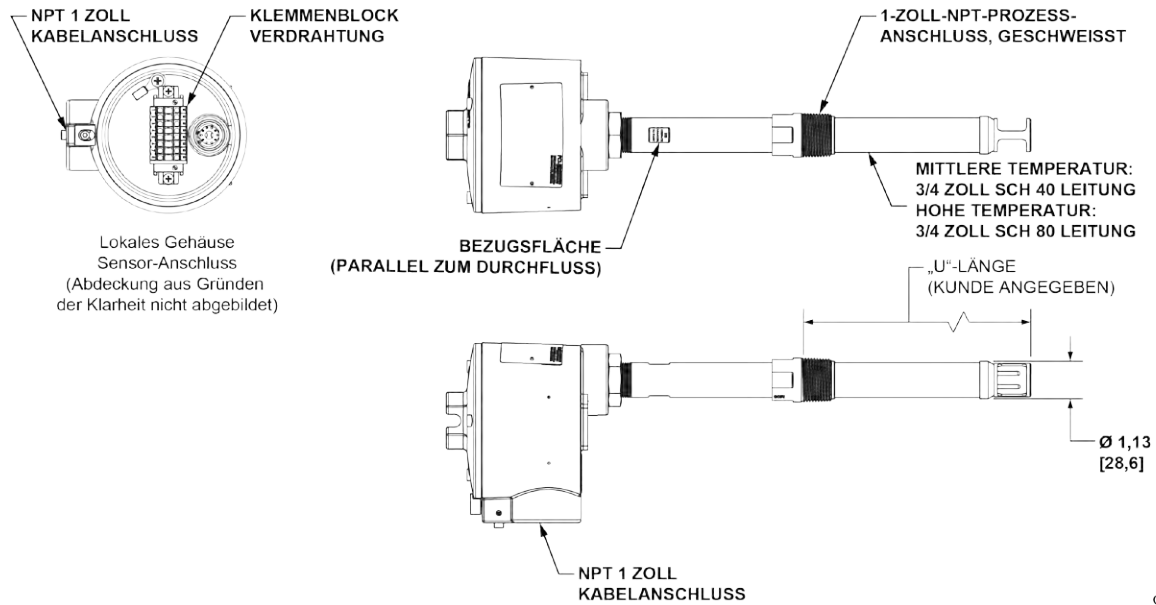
Einzelpunkt, feste geschweißte 1-Zoll-NPT-Prozessanschluss
